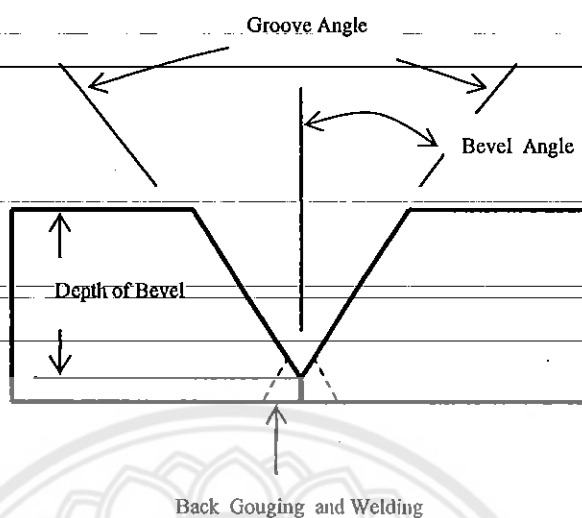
แสดง Double V Double Side Weld [2]
